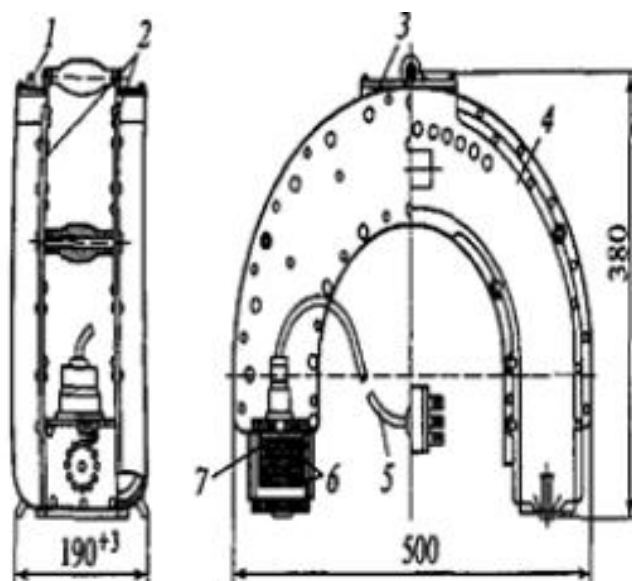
Магнитно-порошковый дефектоскоп: 1 – выключатель, 2 – сердечник, 3 – клеммовый щиток, 4 – корпус, 5 – трехжильный кабель, 6, 7 – намагничивающая и дополнительная катушки
